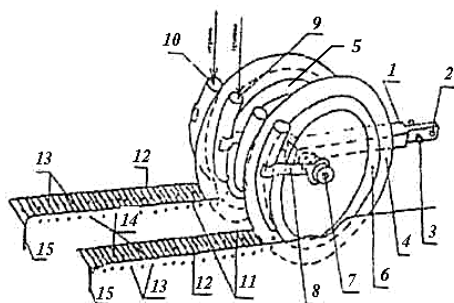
Технический процесс работы комбинированного двухдискового сошника с разновеликими ребрами: 1 – корпус; 2 – отверстие; 3 – болт; 4 – диск; 5, 6 – реборды-бороздкообразователи-уплотнители; 7 – ось; 8 – пластина; 9, 10 – семянаправители; 11, 12 – бороздки; 13, 14 – семена зерновых и трав; 15 – щели
